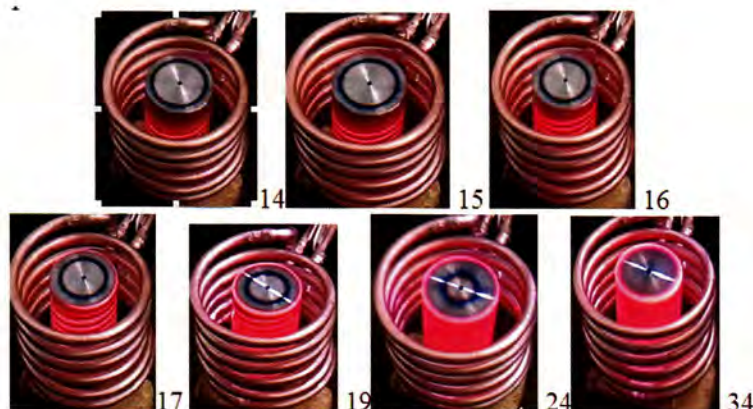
Полосатый нагрев цилиндра из магнитной стали в многовитковом индукторе
